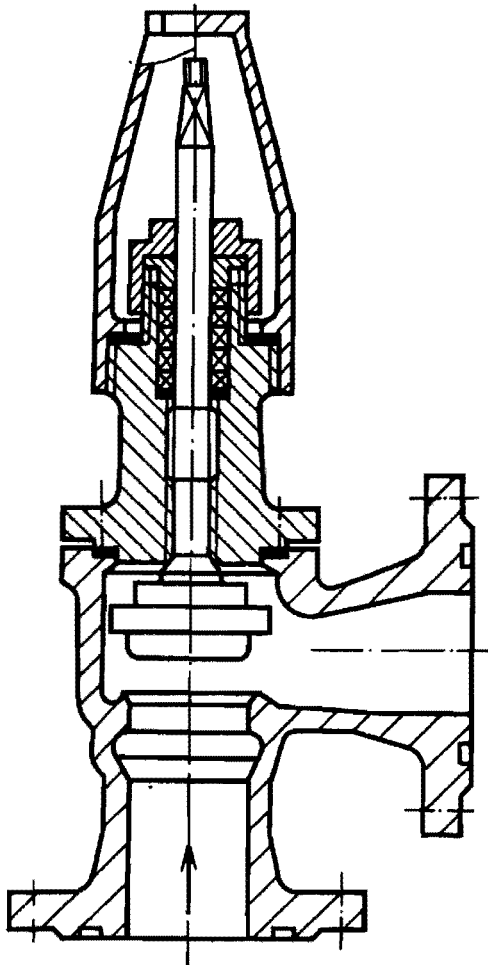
Угловой запорный вентиль с защитным колпаком (Herl, ФРГ)
